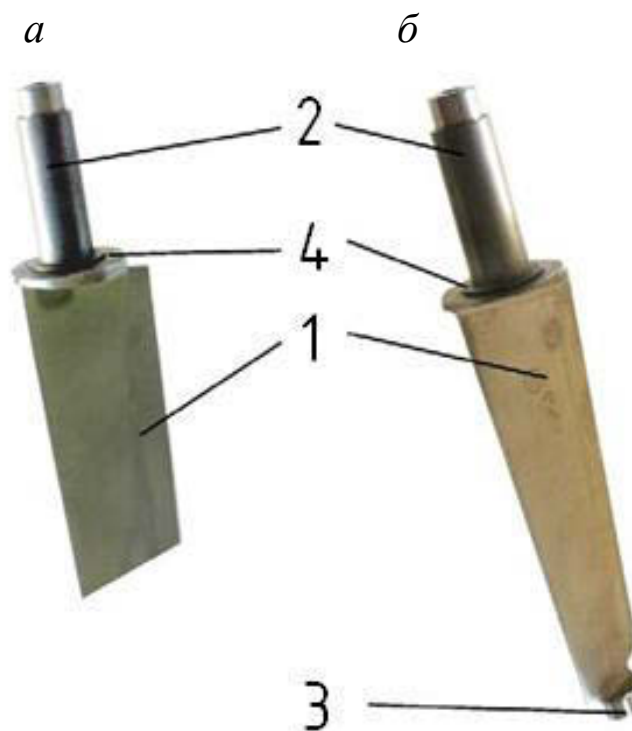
Поворотная лопатка НА: *а* – консольная; *б* – двухопорная; 1 – перо; 2 – наружный цилиндрический хвостовик; 3 – внутренний цилиндрический хвостовик; 4 – упорный торец
